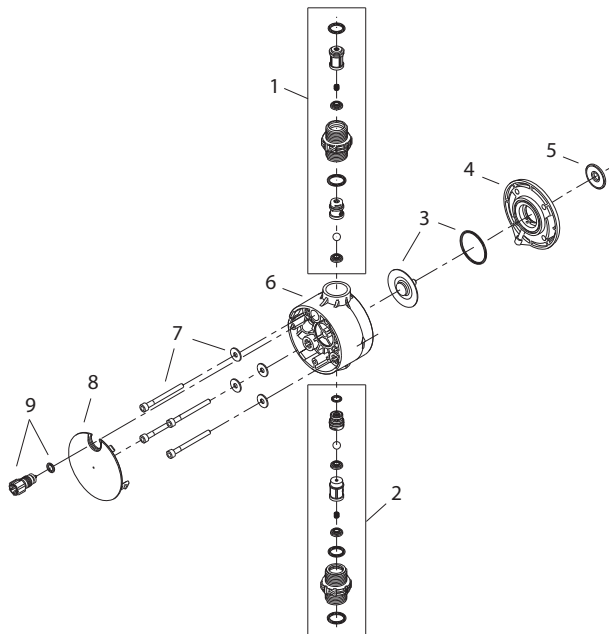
Дозирующая головка DDE: сборочный чертёж
